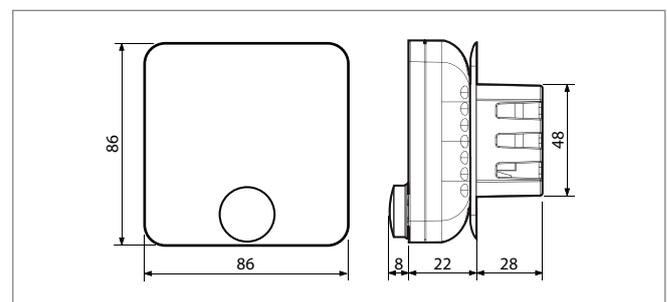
Dimensions pour l'élément de commande zone en cas de montage encastré (dimensions en mm)
